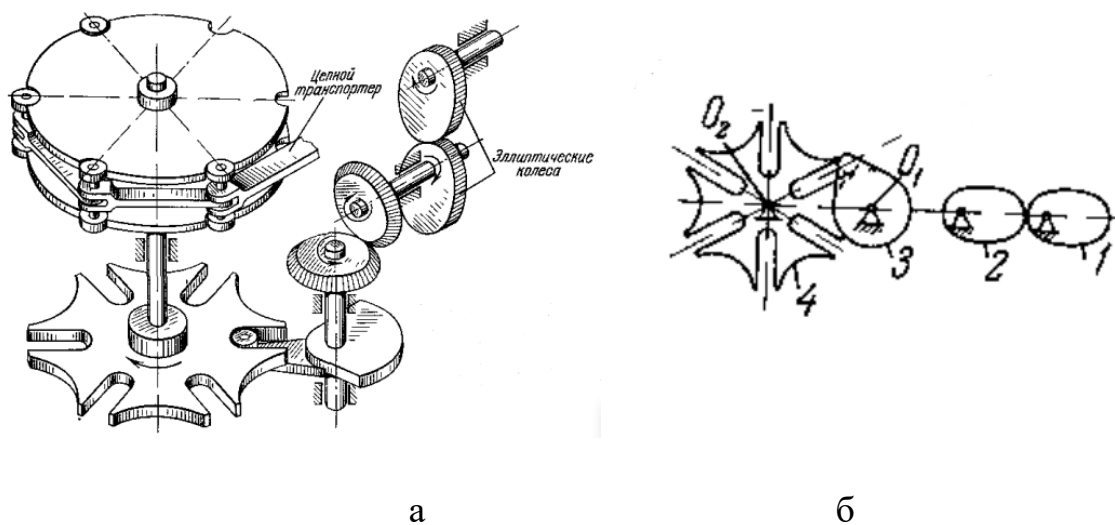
Привод блокообрабатывающей машины [8]
